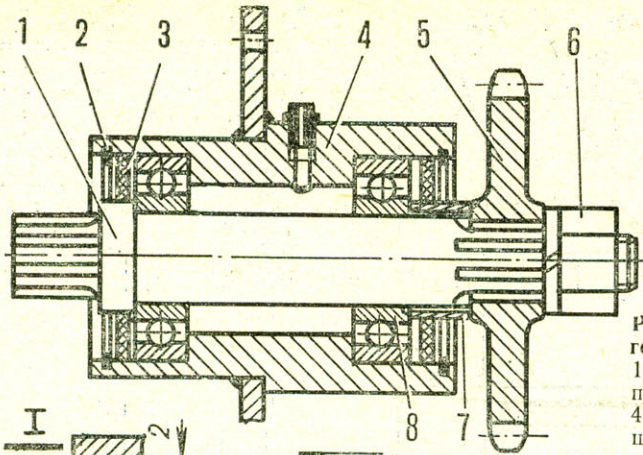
Конструкция ведущего вала микротрактора «САП»: 1 — ведущий вал, 2 — стопорное кольцо, 3 — сальник, 4 — корпус крепления ведущего вала, 5 — ведущая звездочка, 6 — гайка, 7 — втулка, 8 — шариковый подшипник № 205.
